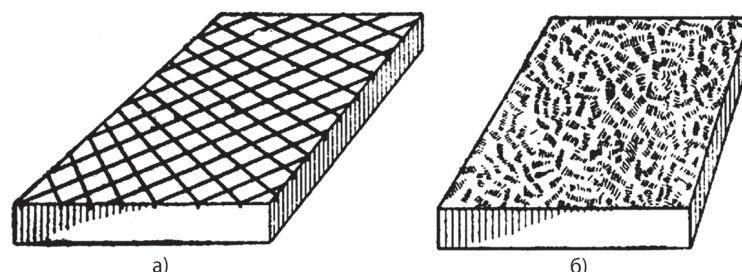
Притиры для обработки плоскостей: а — плита с канавками для грубой притирки; б — плита для чистовой притирки
